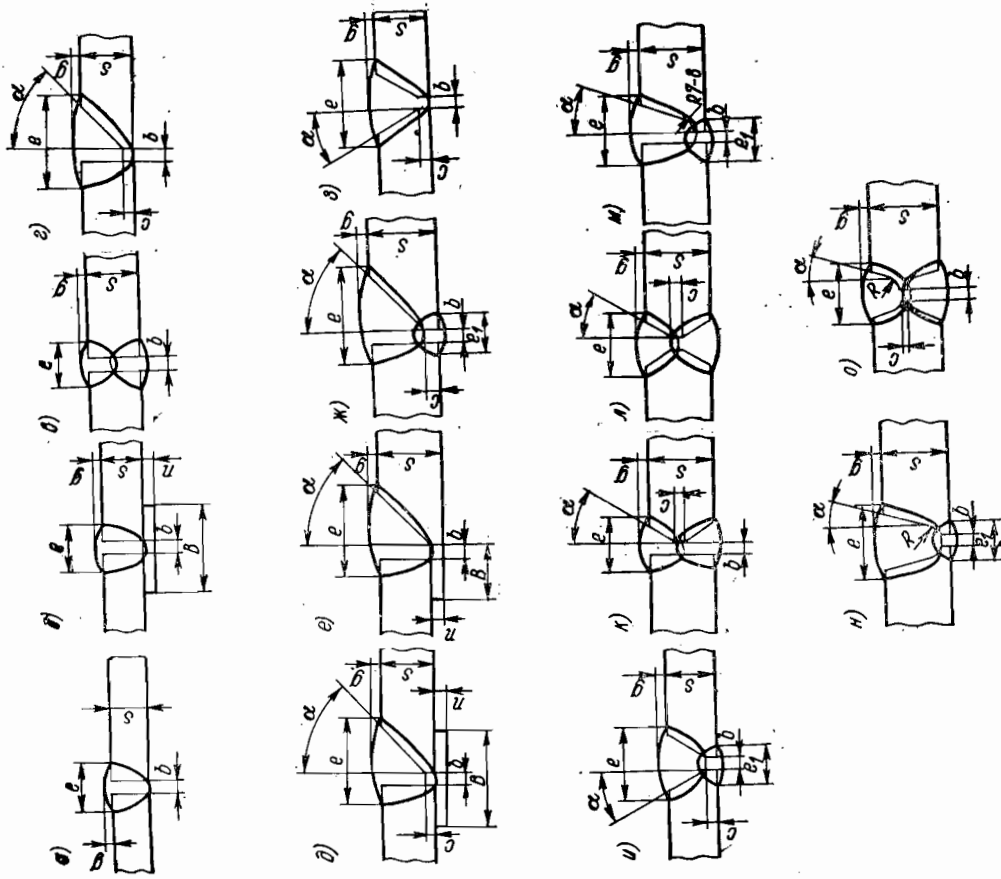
Конструкции стыковых сварных соединений стали, выполненные электродуговой сваркой: а — односторонние без скоса кромок; б — двусторонние без скоса кромок со съёмной или остающейся подкладкой; в — двусторонние без скоса кромок; г — односторонние со скосом одной кромки; д — односторонние со скосом одной кромки и со съёмной или остающейся подкладкой; е — односторонние замковые со скосом одной кромки; ж — двусторонние со скосом одной кромки; з — односторонние со скосом двух кромок; и — двусторонние со скосом двух кромок; к — двусторонние с двумя скосами одной кромки; л — двусторонние со скосами двух кромок; м — двусторонние с двумя криволинейными скосами одной кромки; н — двусторонние с четырьмя криволинейными скосами двух кромок; о — двусторонние с четырьмя криволинейными скосами двух кромок
